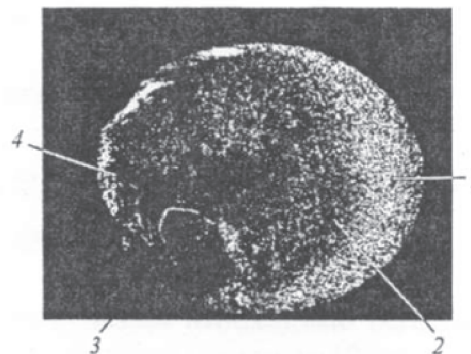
Фрактография усталостного разрушения сварного соединения стали 30ХГСА со сталью ДИ-8
